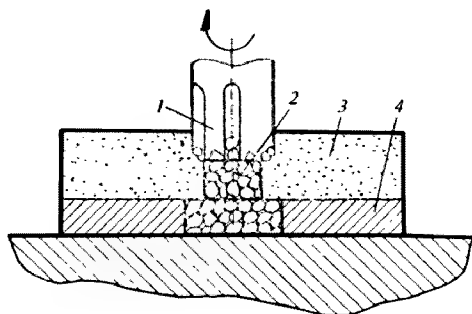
Схема обработки посадочного отверстия круга с использованием чугуна зерно:
